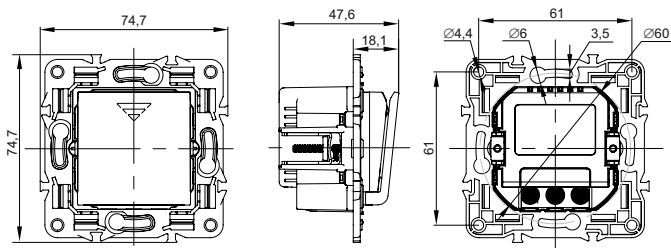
Габаритные и установочные размеры выключателя / Figure 2 – Overall and installation dimensions of the switch / 2 сурет – Ажыратқыштың габариттік және орнату өлшемдері / Figura 2 – Dimensiunile generale și de instalare ale întrerupătorului
